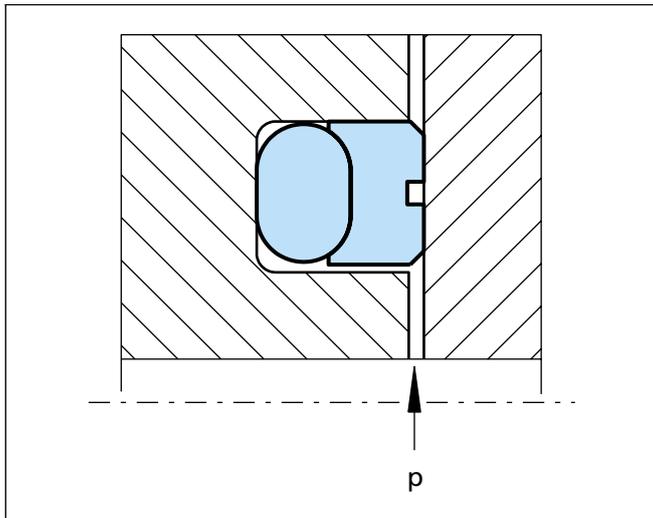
Axialwirkender Turcon® Roto Glyd Ring®
